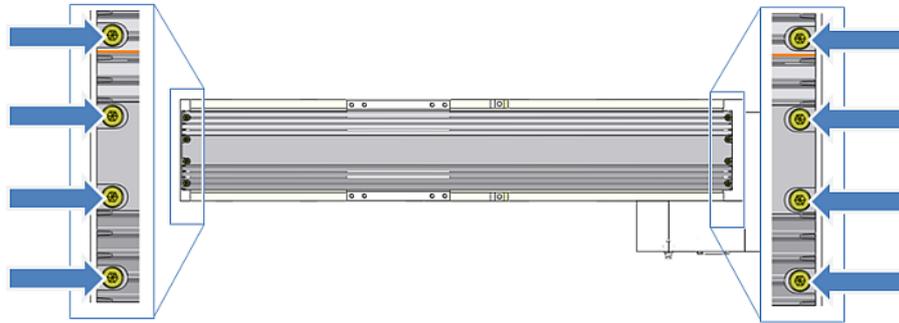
Lage der Schrauben für die Befestigung der Schutzabdeckung
